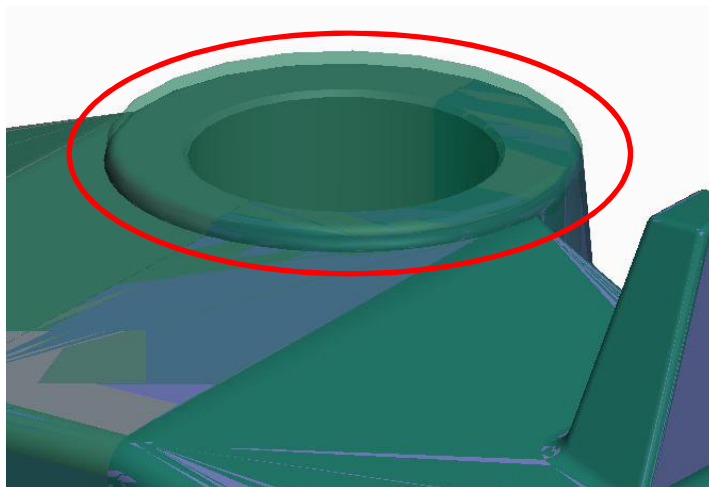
Sección de mecanizado de tija inferior mediante fresa plana de diámetro 10 mm .
